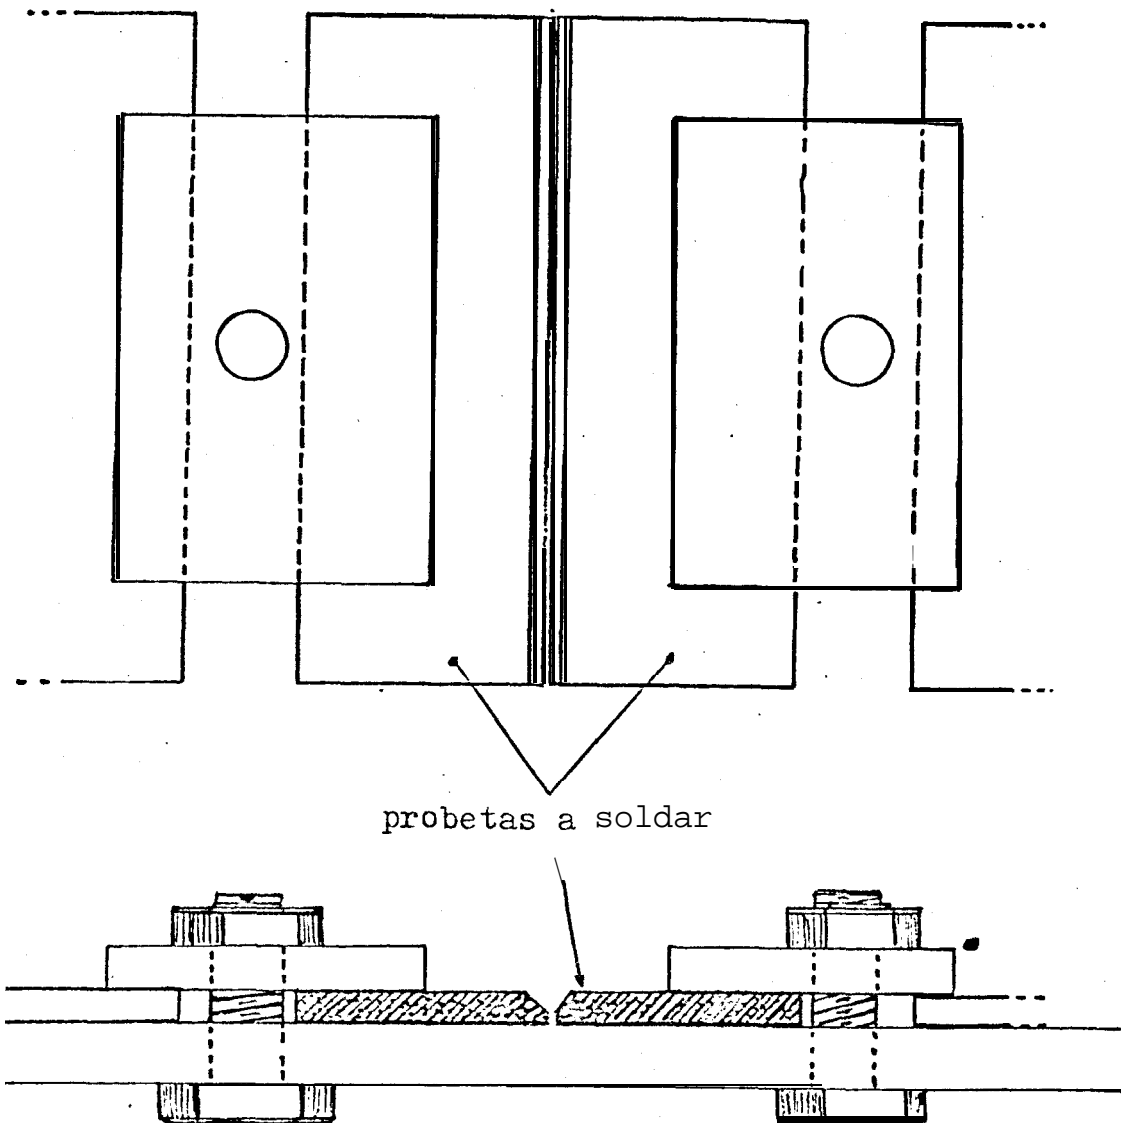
Ensamble de sujeción para el proceso de soldadura con restricción.
